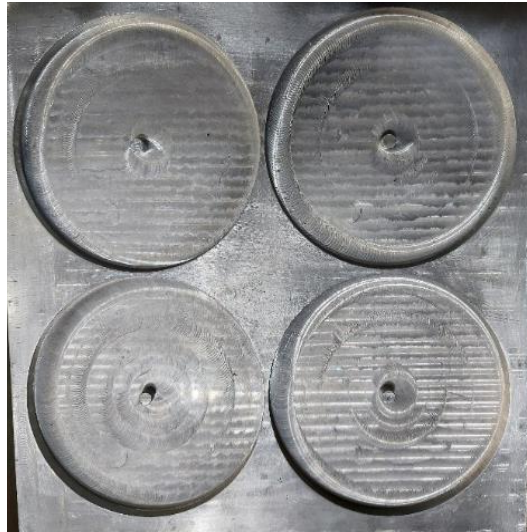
Molde mecanizado en la maquina CNC de la empresa "ColorPlast".
